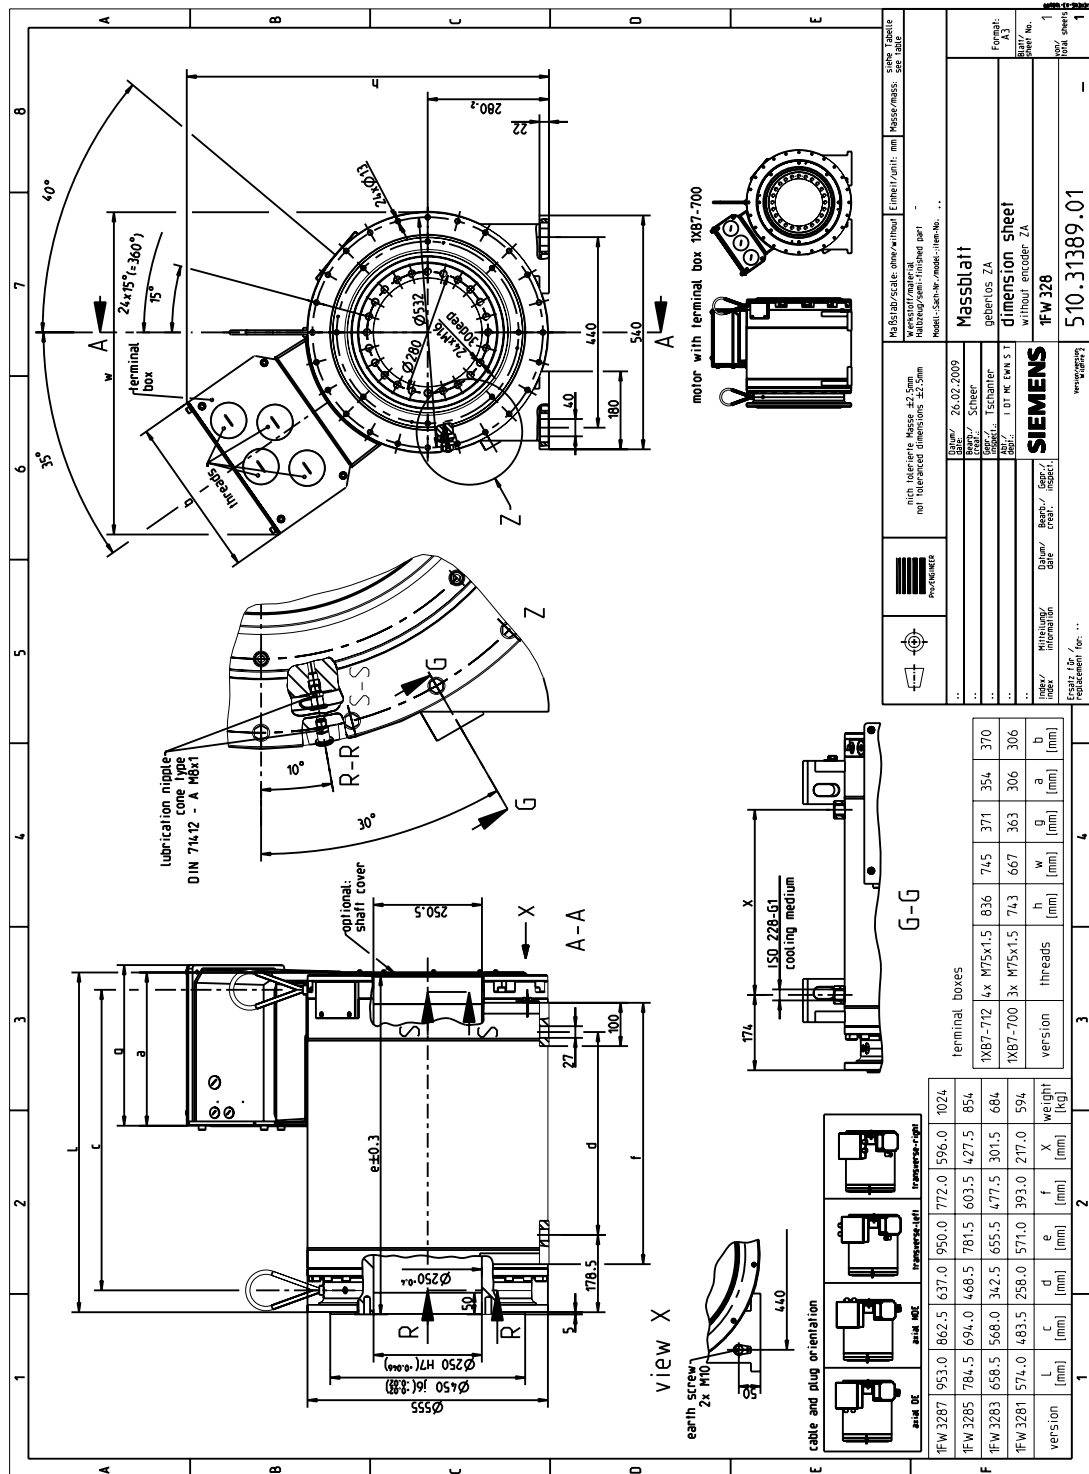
Torque-motor completo 1FW328□, sin encóder
